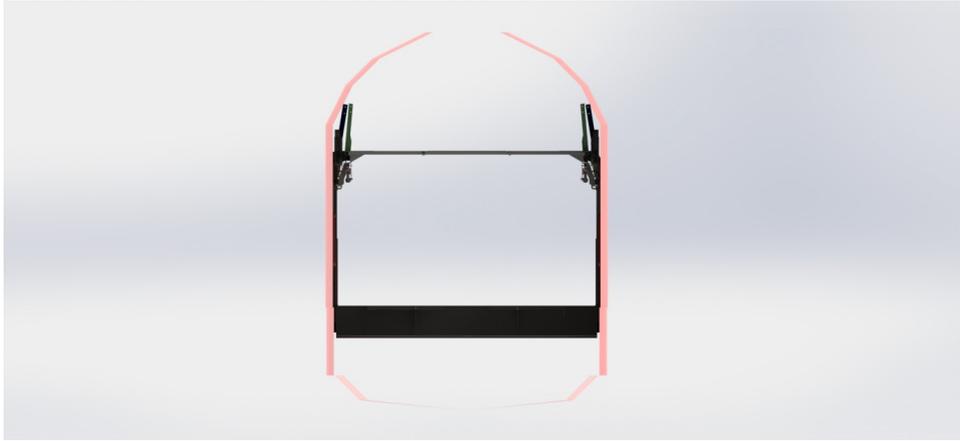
Vista transversal del gálibo con el vagón modificado.
